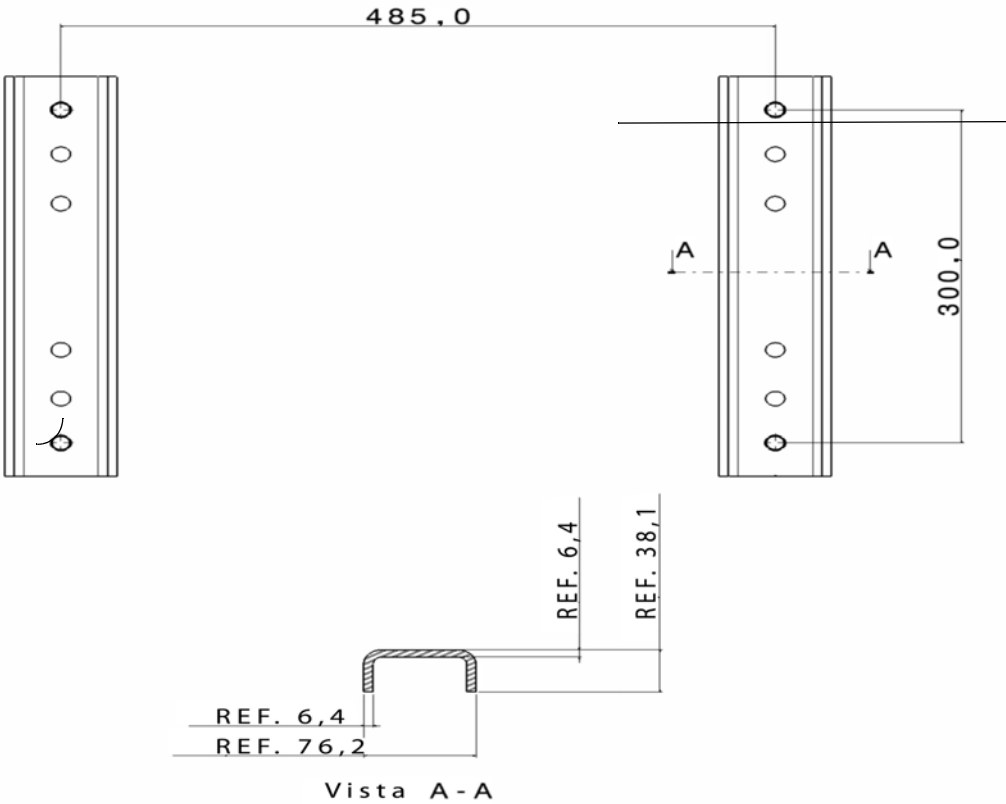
Base de montaje (TT300, TT350, TT400 y TT500)
